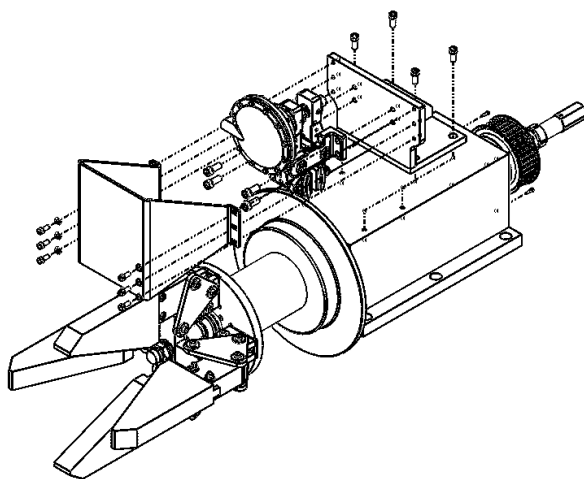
Perspetiva isométrica explodia do desenho de conjunto “Assembly final chumaceira BF”.
